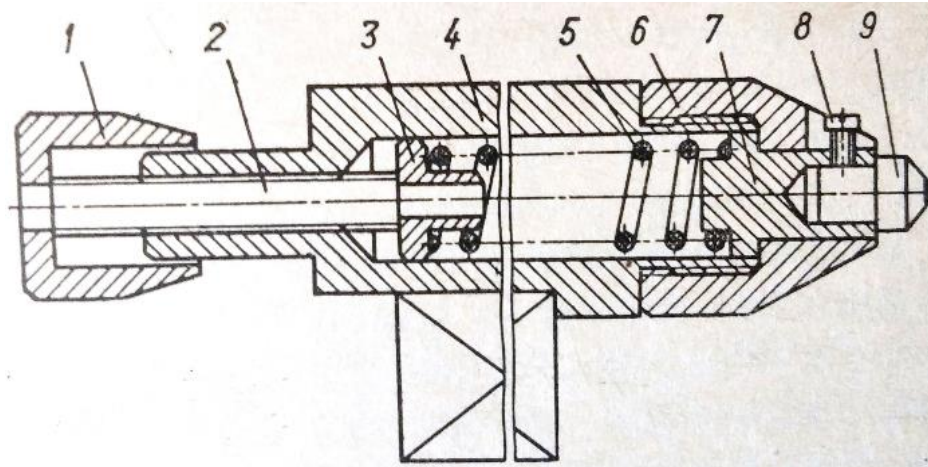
Пристрій для вигладжування зовнішніх циліндричних поверхонь: 1 – маховик для регулювання зусилля, 2 – гвинт мікрометричний. 3 – упор, 4 – корпус, 5 – пружина, 6 – гайка, 7 – плунжер, 8 – гвинт, 9 – вигладжувач
